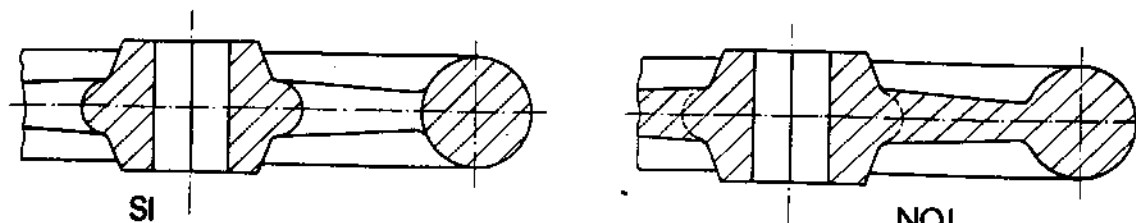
Le razze non si sezionano quando il piano di sezione è longitudinale.
